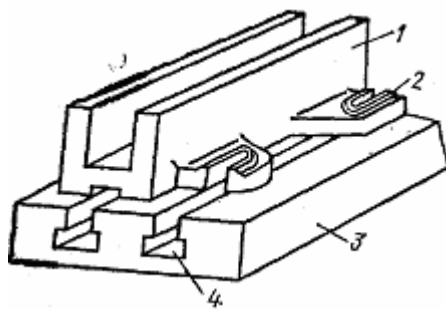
Елементи корпусів для кріплення пристроїв на столі станка
